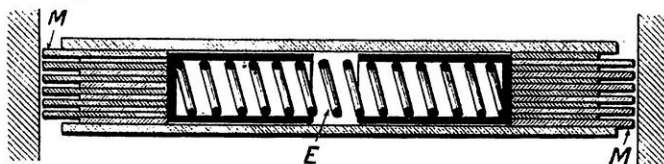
LAMELLES D'ÉTANCHÉITÉ
